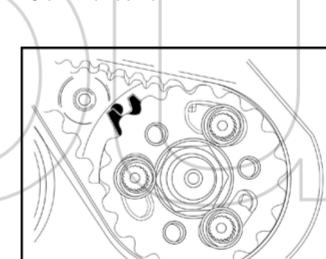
Ruotare il drive shaft clockwise by two turns, then refit all the tools to check the correct timing. If you can't insert the high pressure jig, check that there is only a slight offset.
